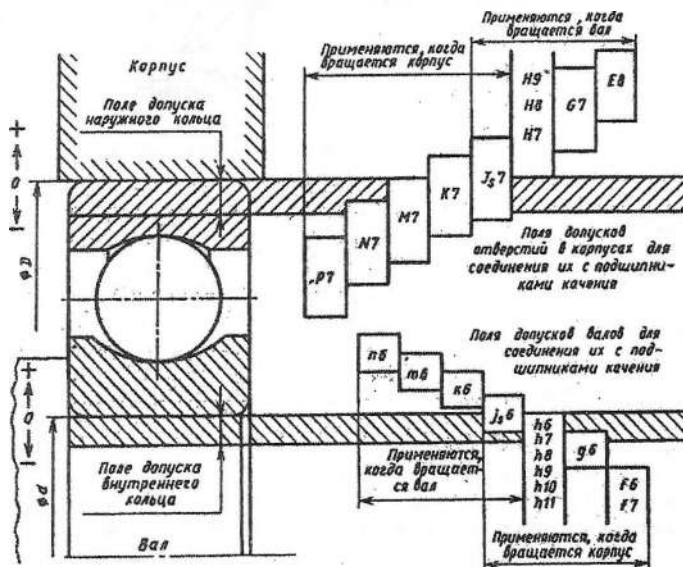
Схема расположения полей допусков на внутренний и внешний диаметры подшипников качения (на вал и в корпус).
